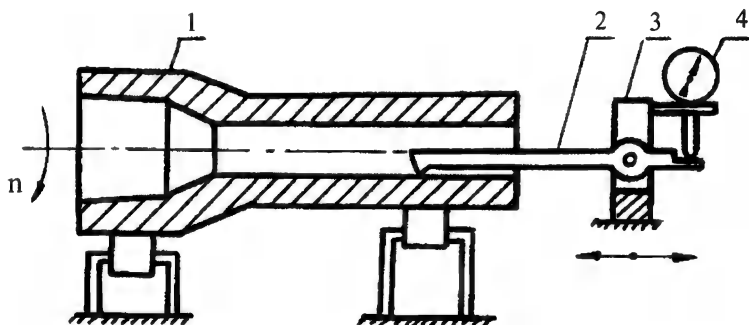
Рычажный прибор для контроля ровности поверхности канала ствола: 1 - ствол, 2 - рычаг, 3 - стойка, 4 - индикатор
